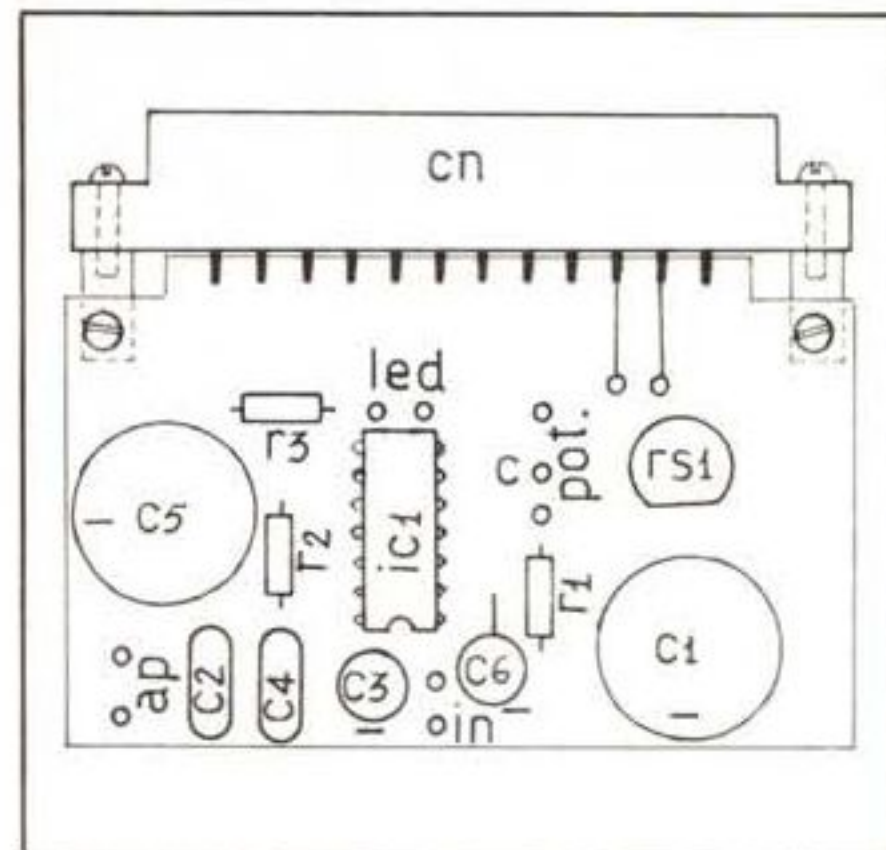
Piano di assemblaggio dei componenti sul circuito stampato.
